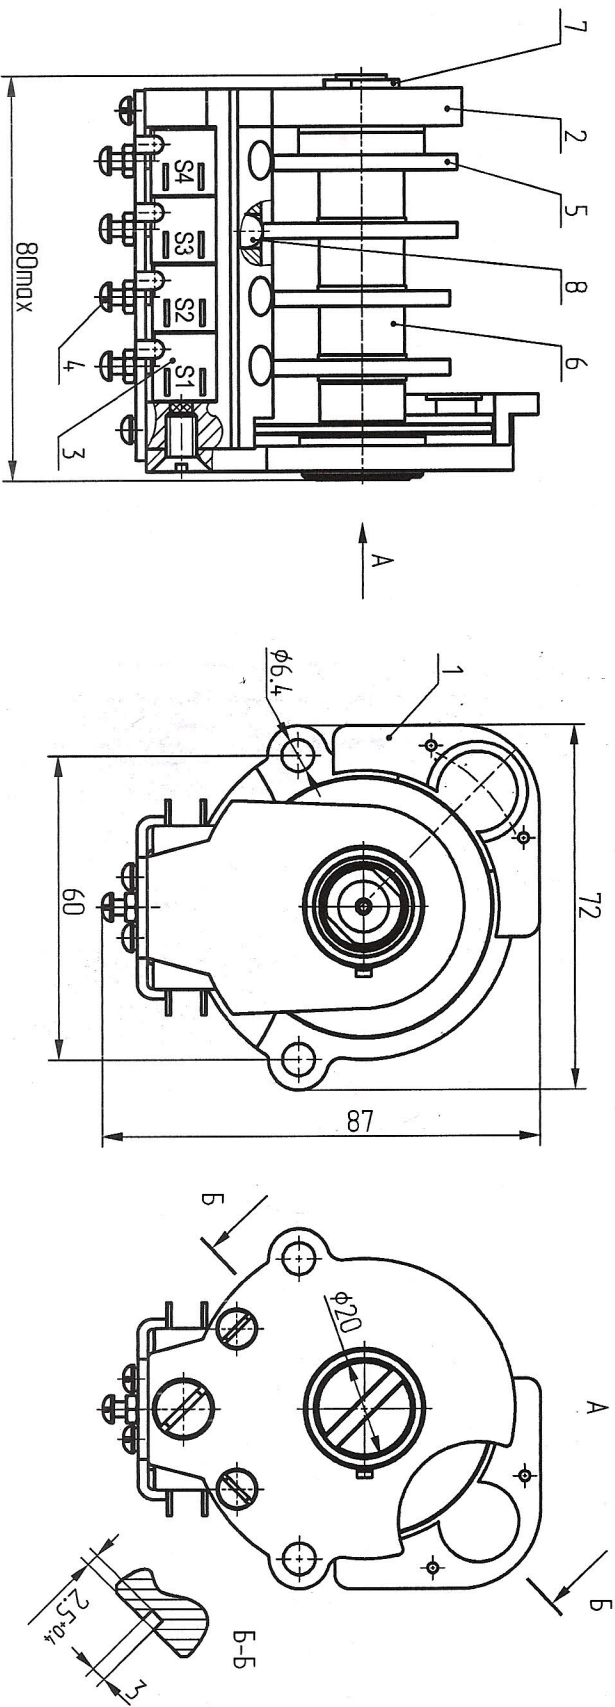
Общий вид, габаритные и присоединительные размеры блоков БКВ, БКВ-Ш для однооборотных механизмов и приводов
